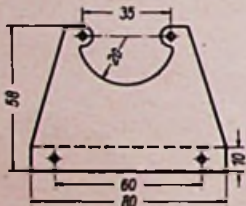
Montagewinkel für Gleichrichterröhre AZ 11
